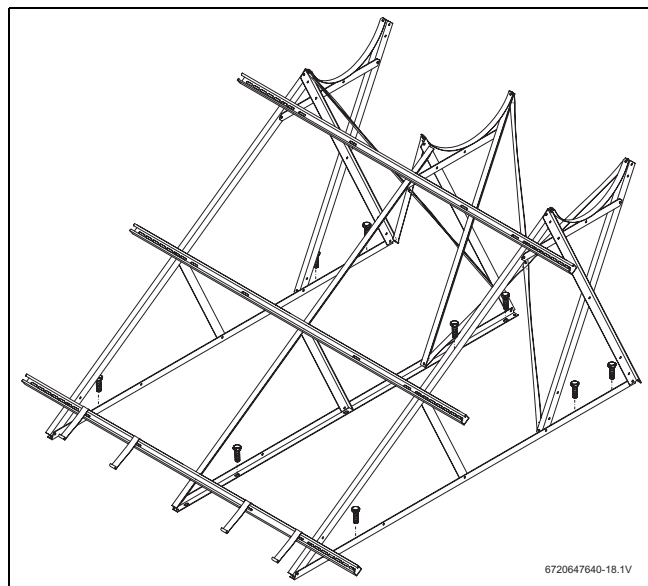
Connexion au toit pour le système toit terrasse (ici pour système 300 I)
